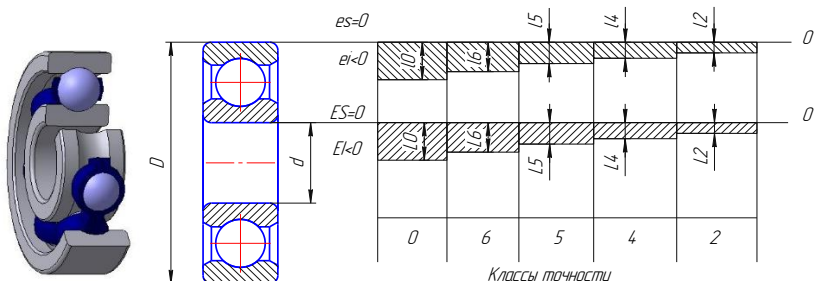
Схема расположения интервалов допусков наружного и внутреннего колец подшипников различных классов точности (0 – нормальный класс точности)
